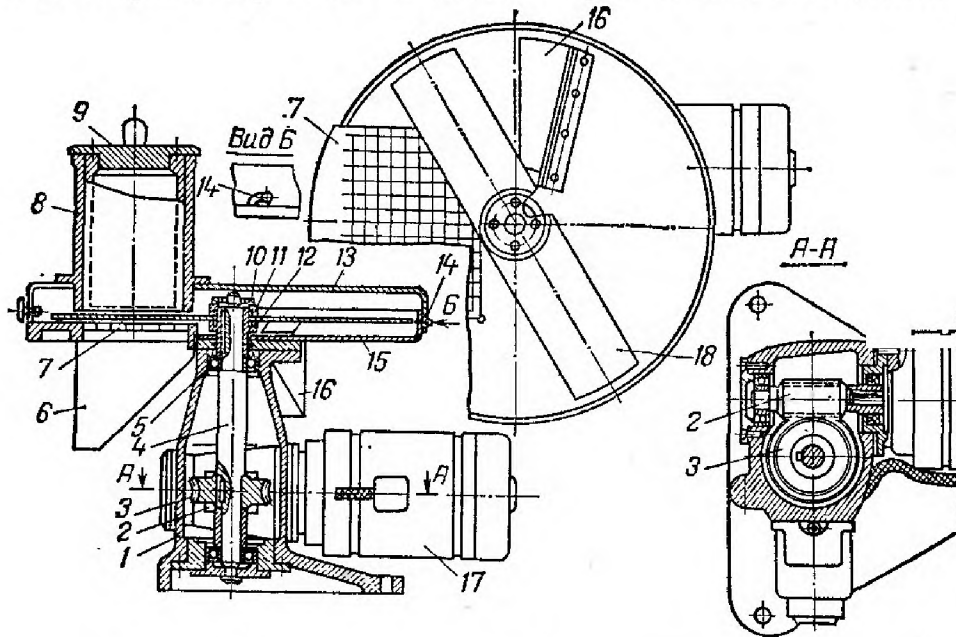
Машина для нарізання варених овочів МРОВО-160: 1 – редуктор черв'ячний; 2 – черв'як; 3 – колесо черв'ячне; 4 – вал вихідний; 5 – підшипники кочення; 6 – лотік розвантажувальний; 7 – ножова решітка; 8 – циліндр завантажувальний; 9 – вантаж-штовхач; 10 – гайка фасонна; 11, 12 – втулки; 13 – кришка; 14 – штифт; 15 – тарілка; 16 – лотік для видалення крихти; 17 – електродвигун; 18 – ніж прямолінійний
